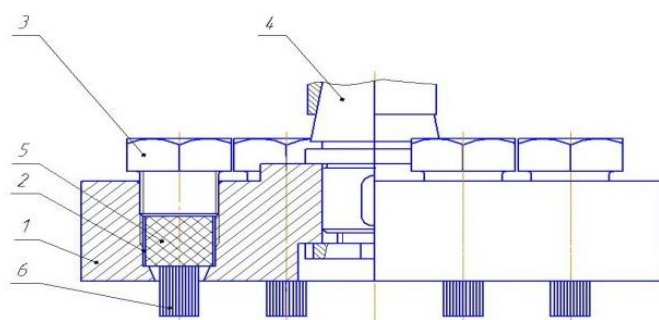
Иглофреза торцовая сборной конструкции со сменными режущими элементами состоит из: 1 - корпус сборной торцовой иглофрезы, 2 - отверстие для установки сменного режущего элемента (держателя ворса), 3 - болт для крепления сменного режущего элемента (держателя ворса), 4 - фрезерная оправка для крепления в шпиндельном узле станка, 5 - сменный режущий элемент (держатель ворса), 6 – ворс, состоящий проволока.
